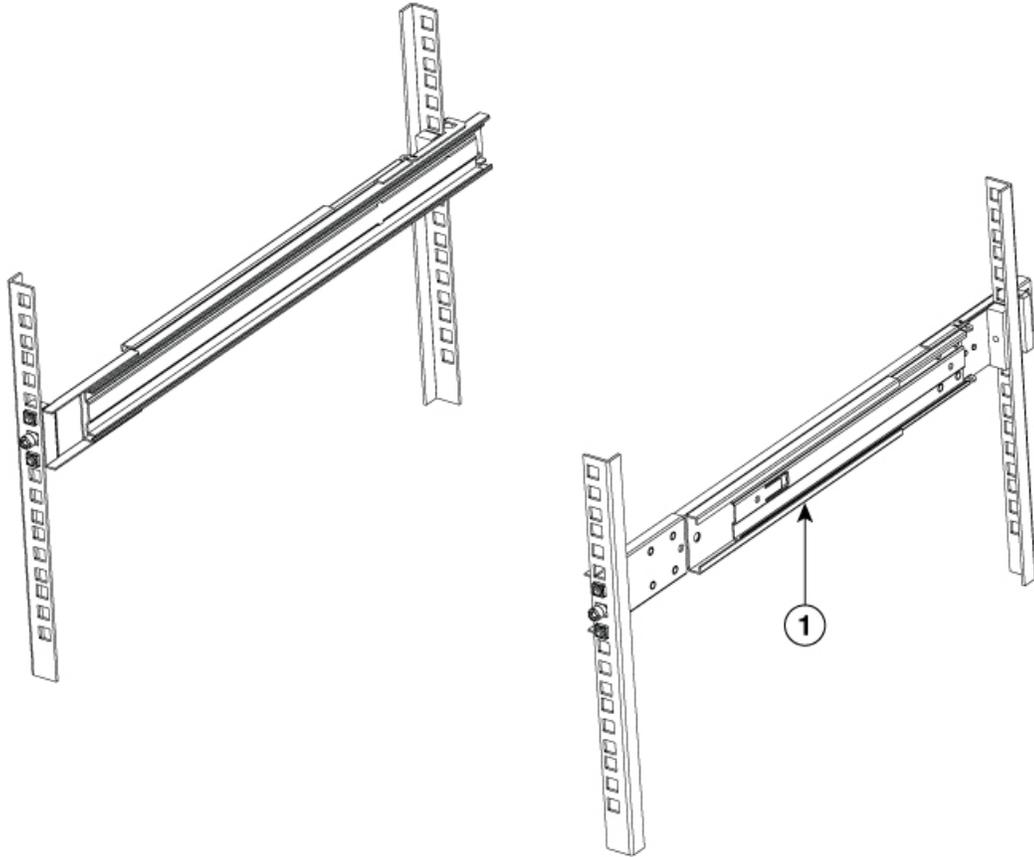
Extremos trasero y delantero (NC55-2RU-ACC-SL2) del miembro del deslizador externo
